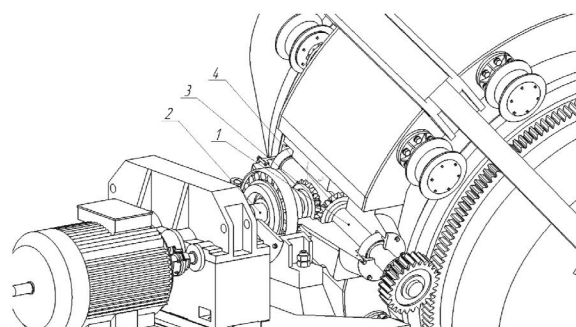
Предложенная конструкция механизма вращения корпуса кислородного конвертера
